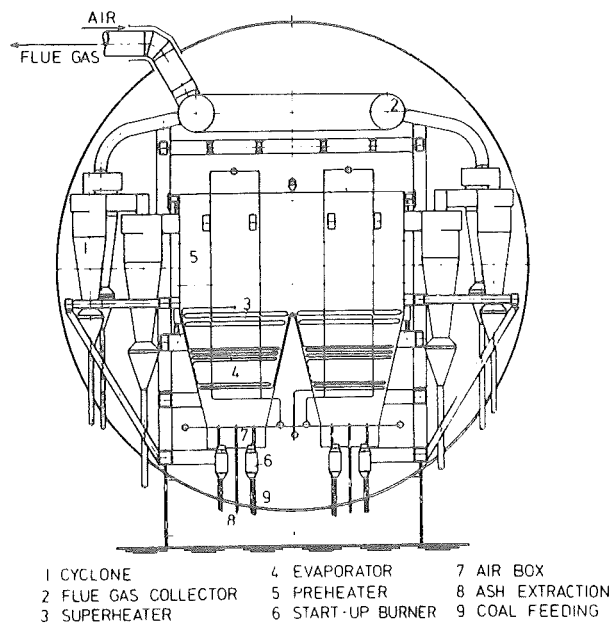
Babcock Planung für DWSF-Dampferzeuger (123)
